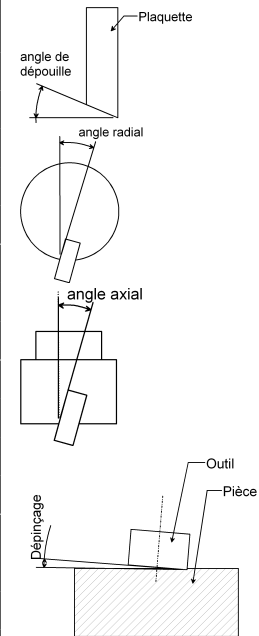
Paramètres d'usinage en ébauche de la face culasse du carter cylindres M9R.
